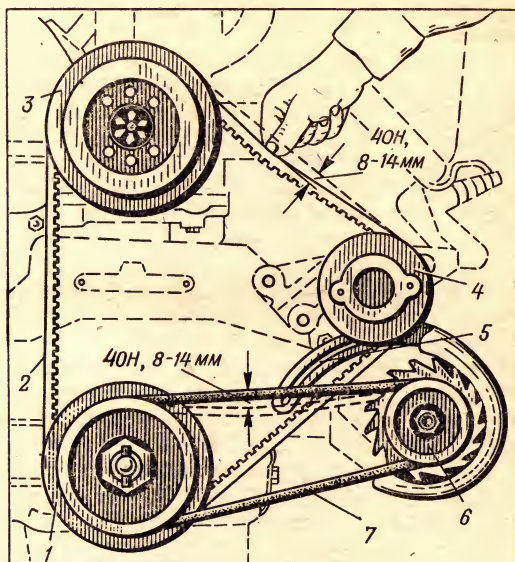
Проверка натяжения приводных ремней вентилятора и генератора двигателей СМД-60 и СМД-62:
